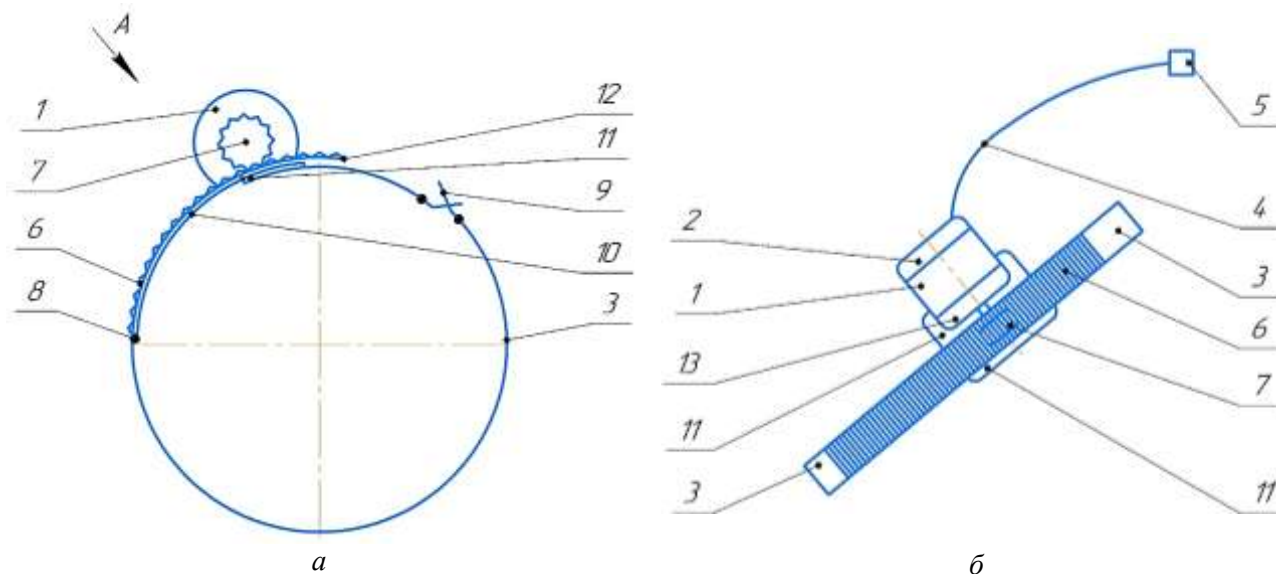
Портативное устройство для зарядки аккумуляторов мобильных приборов: *а* – вид сверху; *б* – вид по стрелке «А»
